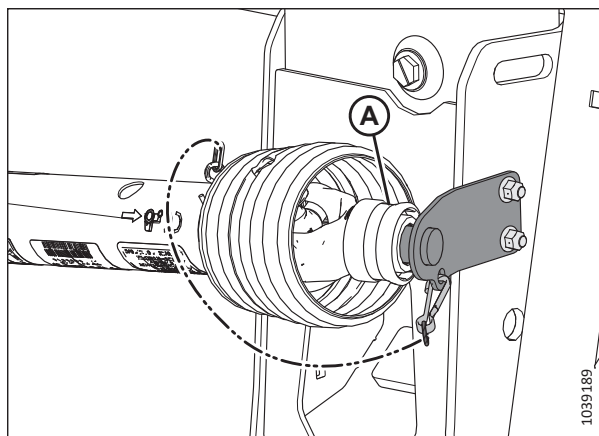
Приводний вал у положенні для зберігання — приводний вал B7038 або B7039
